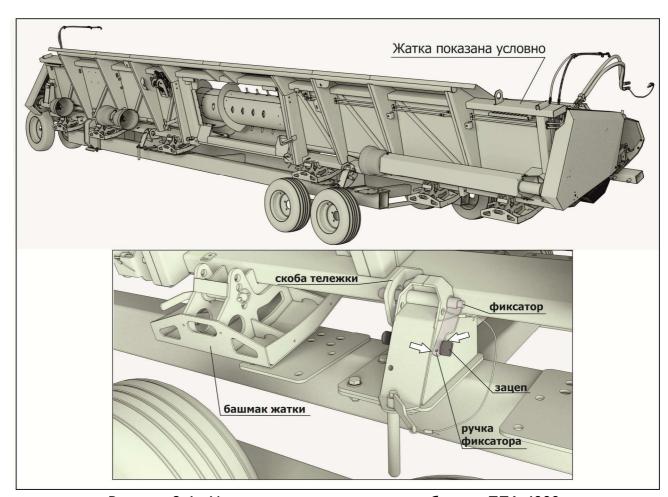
Установка жатки на приспособление ППА-4000
